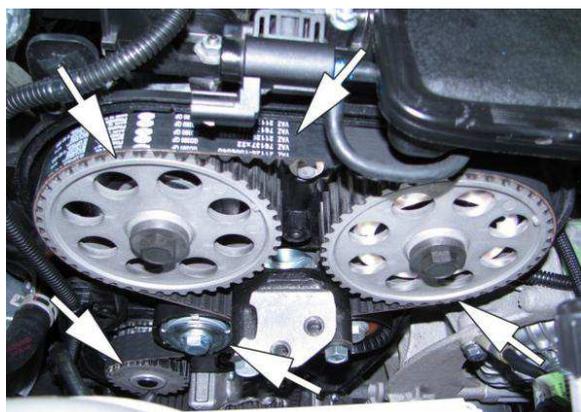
Проверка состояния зубчатого ремня и роликов ГРМ на двигателе ВАЗ-21129
